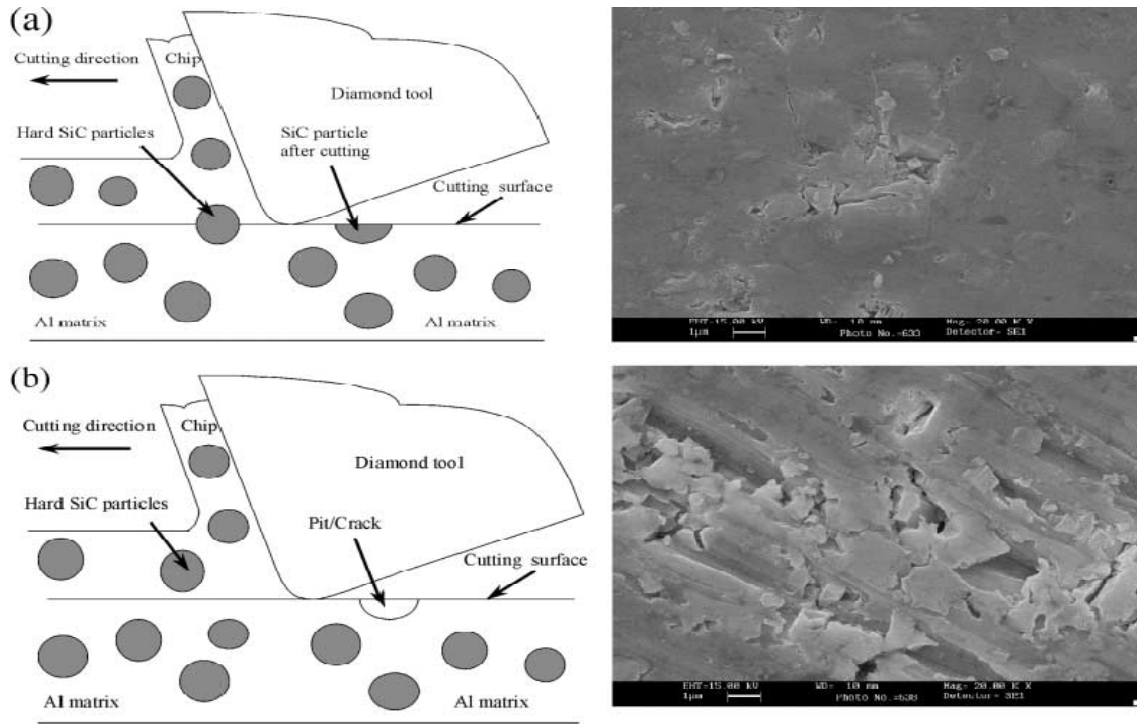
Rugosité de surface en usinage des CsMAIP (a) coupe des particules (b) enlèvement des particules [138].
